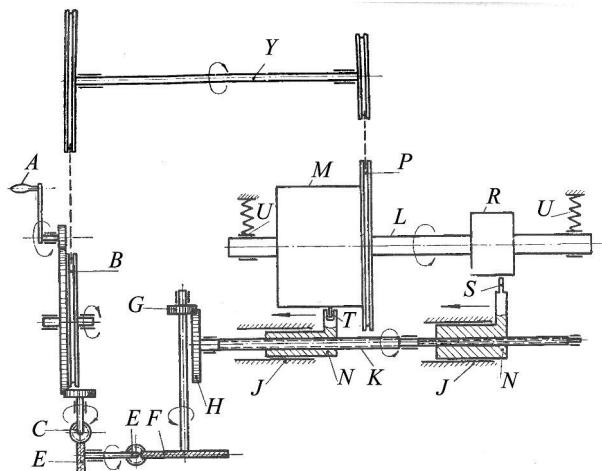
Схема большого токарно-копировального станка Нартова с механизированным суппортом
